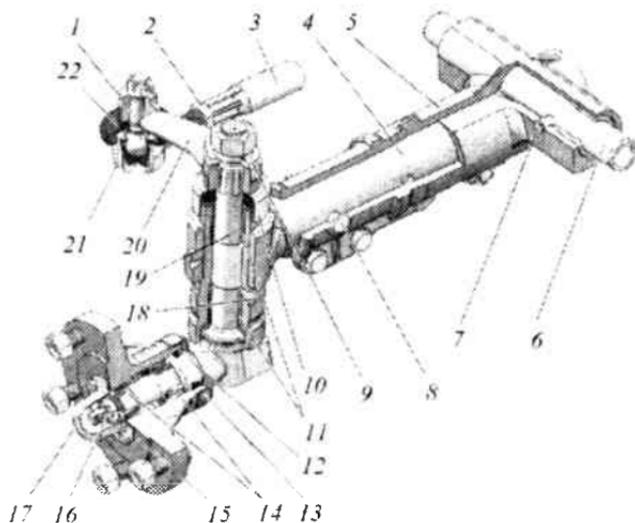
Передний мост универсально-пропашного трактора ТТЗ-80.10: 1 – шаровой палец; 2 – контргайка; 3 – поперечная рулевая тяга; 4 – выдвижной кулак; 5 – труба передней оси; 6 – ось качания; 7, 8 – пальцы; 9 – шайба или кронштейн крыла; 10 – защитный кожух; 11 – втулка; 12 – уплотнительная манжета; 13 – защитная обойма; 14 – роликоподшипники; 15 – ступица; 16 – гайка; 17 – колпак; 18 – масленка; 19 – правая поворотная цапфа; 20 – поворотный рычаг; 21 – корпус шарнира; 22 – защитный чехол
